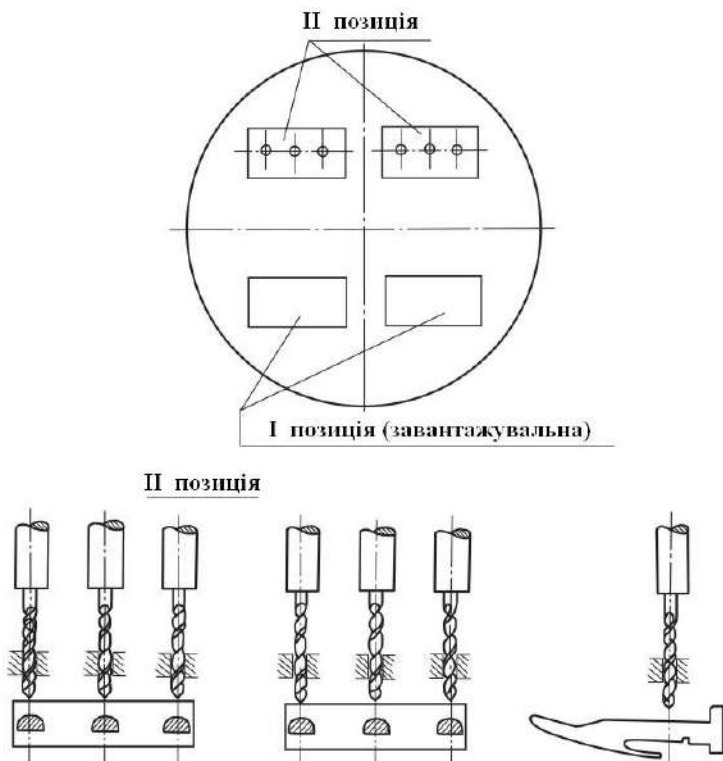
Свердління в деталі трьох отворів на двопозиційному шестишпindelьному свердильному верстаті
